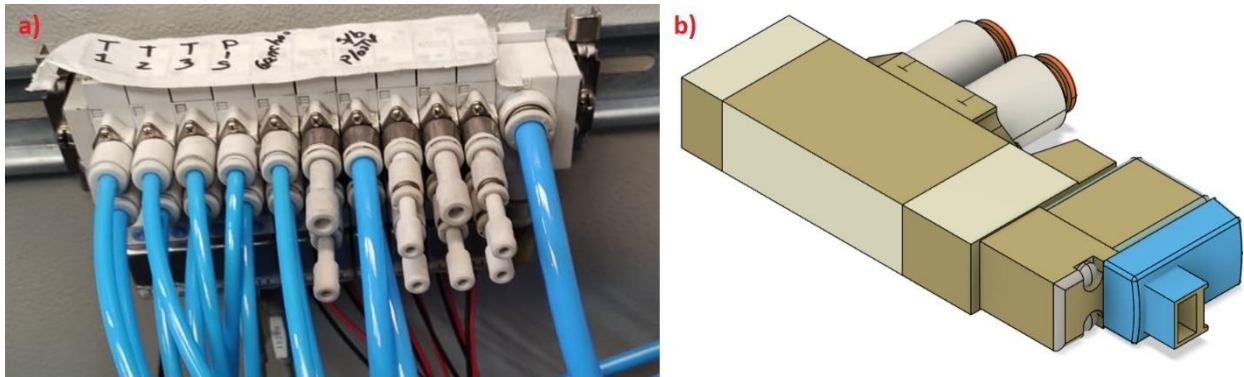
a) Módulo de válvulas SY3160-5LOU-C4. b) CAD válvula SY3160-5LOU-C4.
